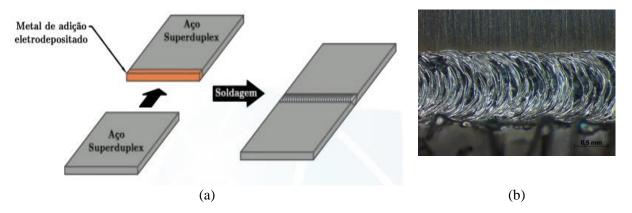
Representação esquemática da soldagem (a) e vista superior do corpo de prova após a soldagem (b).
